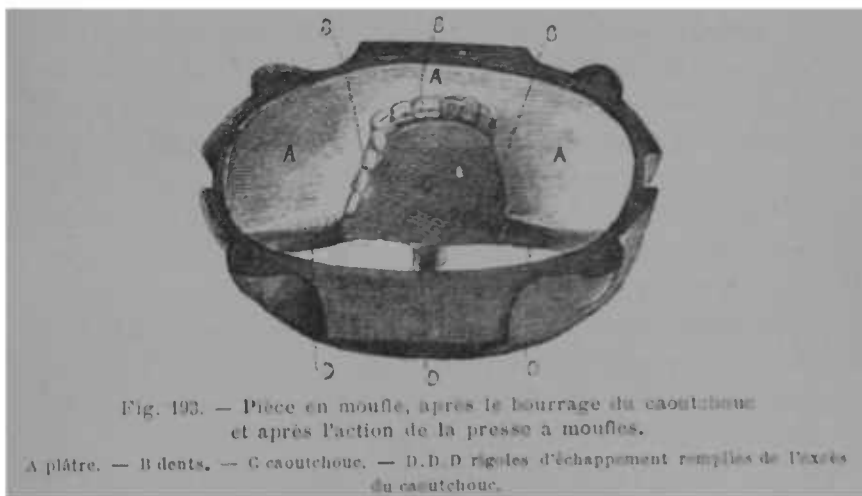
Pièce en moufle, après le bourrage du caoutchouc et après l'action de la presse à moufles.
